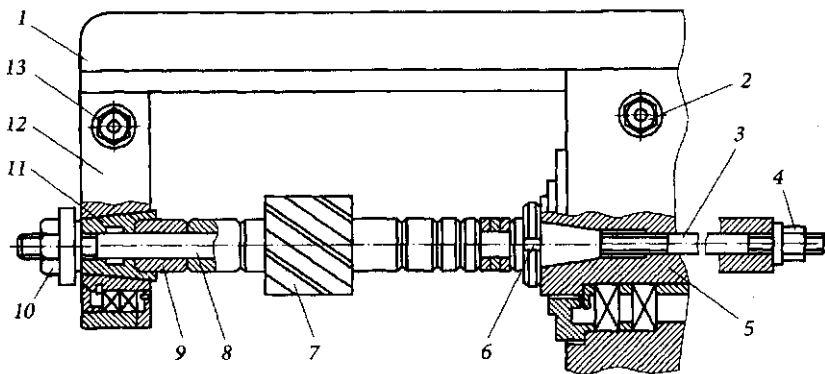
Оправка для установки цилиндрических и дисковых фрез:
